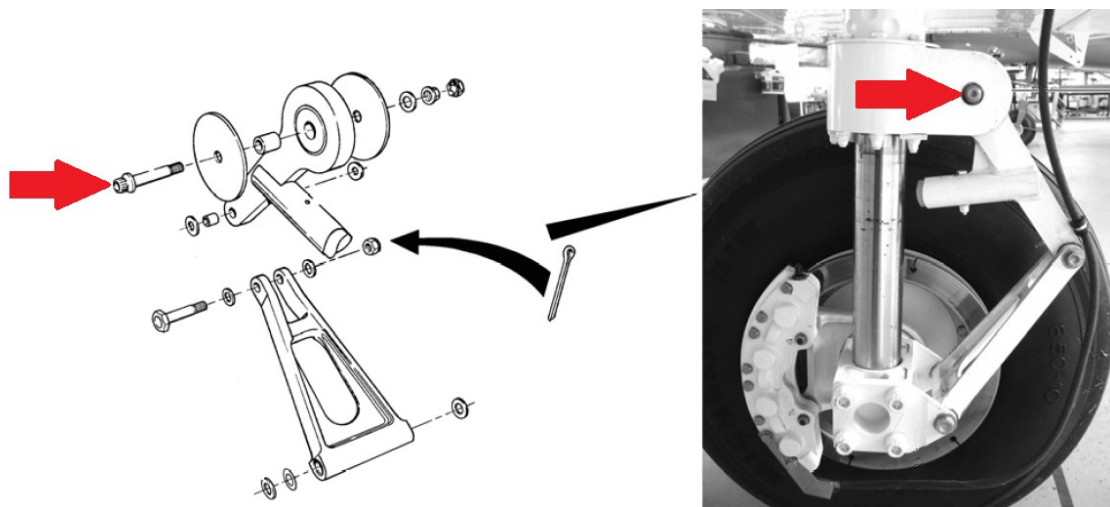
Rechtes Hauptfahrwerkbein mit einer Explosionszeichnung des *torque link*, dessen oberer Befestigungsbolzen (rote Pfeile) verlustig ging (Abbildung aus dem Unterhaltshandbuch des Flugzeugherstellers).
